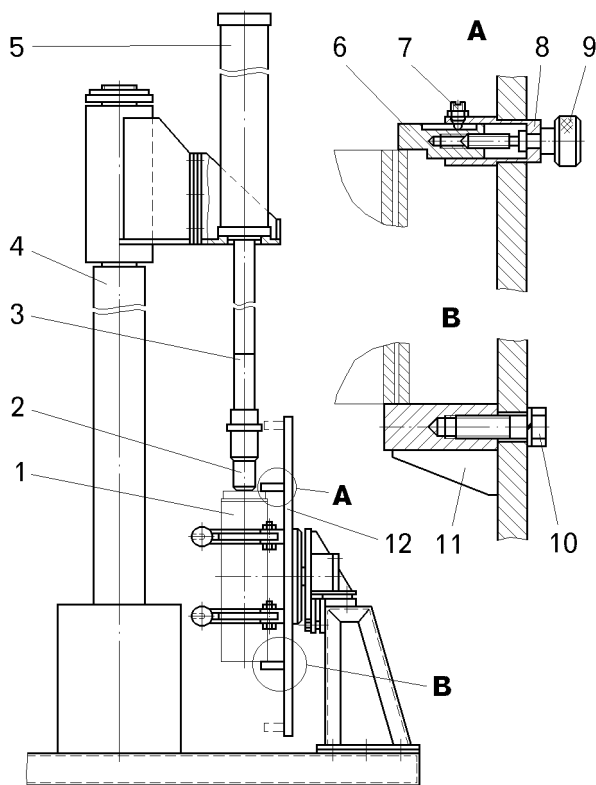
Стенд для разборки и сборки цилиндра опрокидывающего механизма:
